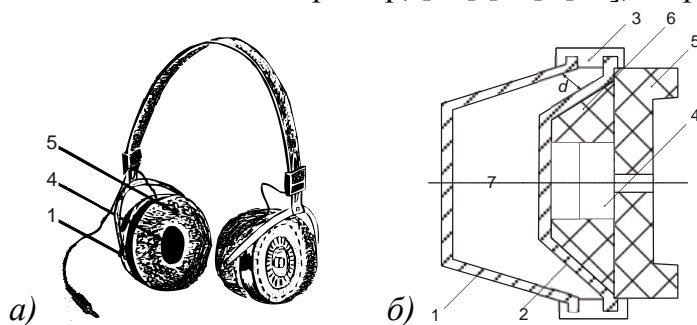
Головной телефон [68]: *а* - внешний вид; *б* – разрез: 1, 2 - внешний и внутренний корпуса; 3 – упругая герметизирующая прокладка; 4 - излучатель
